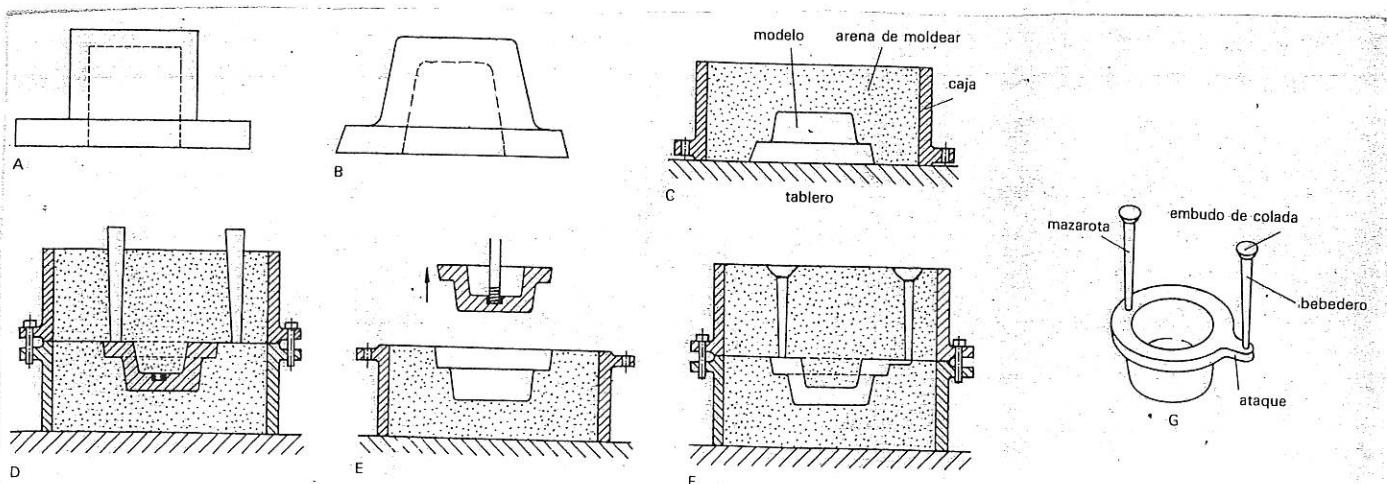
Proceso seguido para el moldeado de una tapa.
